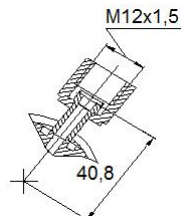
Штуцер для торцевого уплотнения резиновым кольцом с гайкой с метрической резьбой M12x1,5
